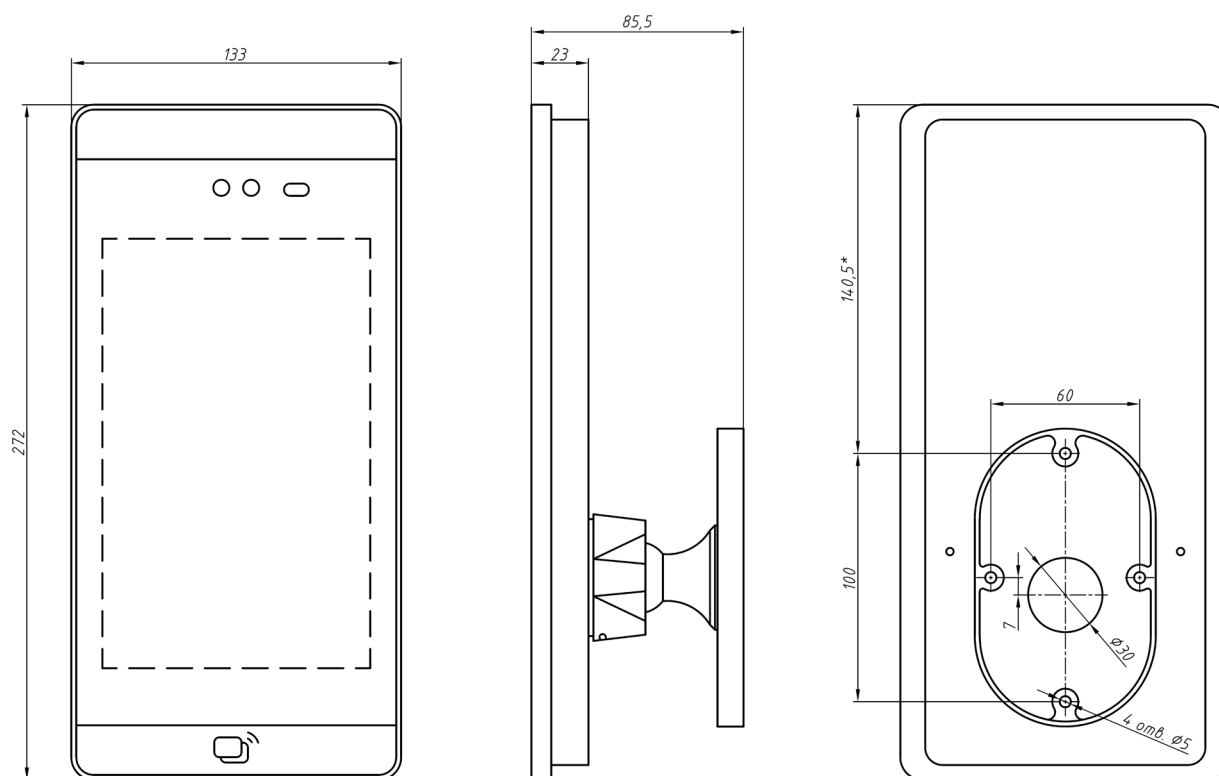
Габаритные размеры и разметка крепежных отверстий терминала R20-Face W8"
